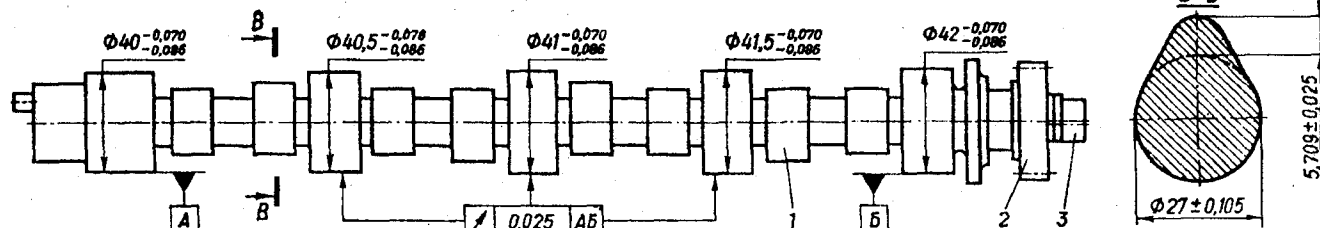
Вал распределительный в сборе: 1 – вал распределительный; 2 – шестерня; 3 – кулачок привода бензинового насоса
